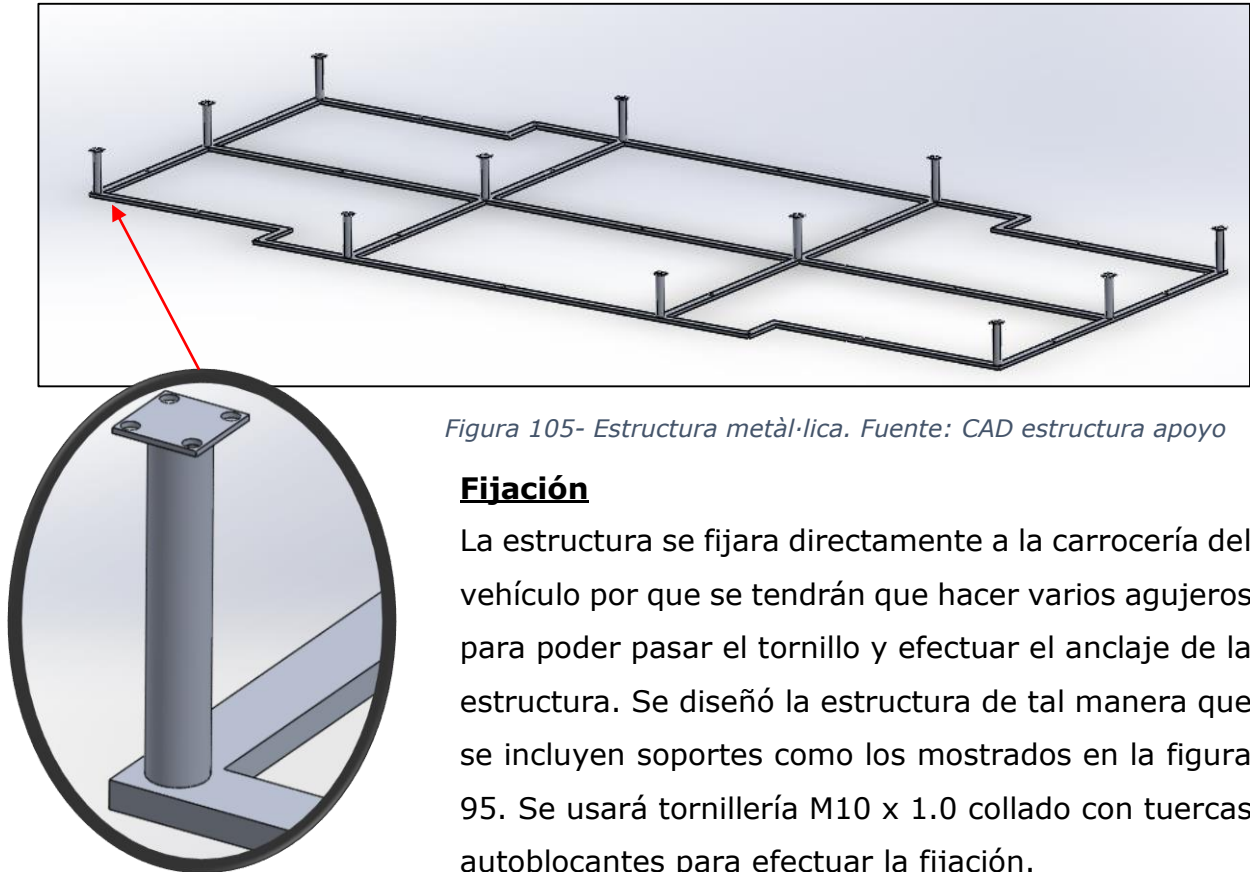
Estructura metálica. Fuente: CAD estructura apoyo
